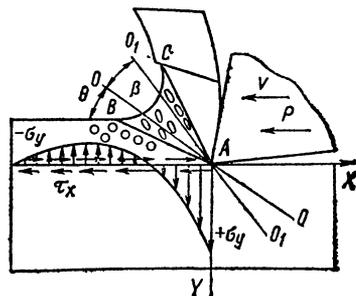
Схема упругонапряженного состояния металла заготовки при обработке резанием
